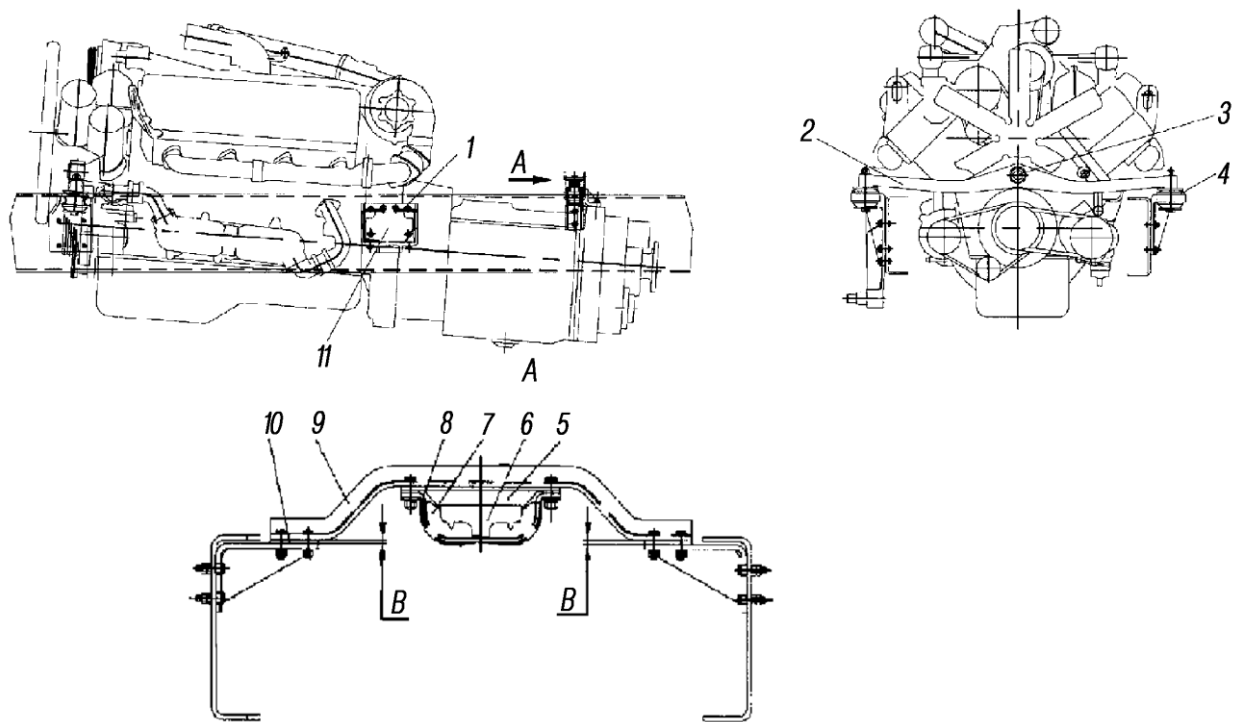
Подвеска силового агрегата ЯМЗ-7511.10:
